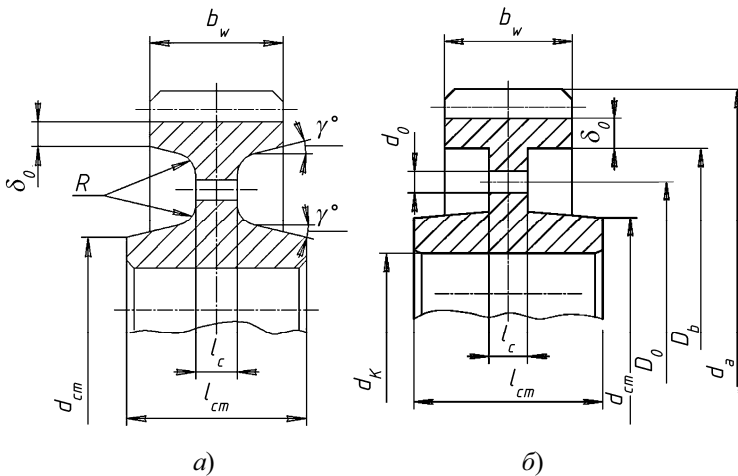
Цилиндрические зубчатые колеса при $150 \text{ мм} \leq d_a \leq 500$ мм:
